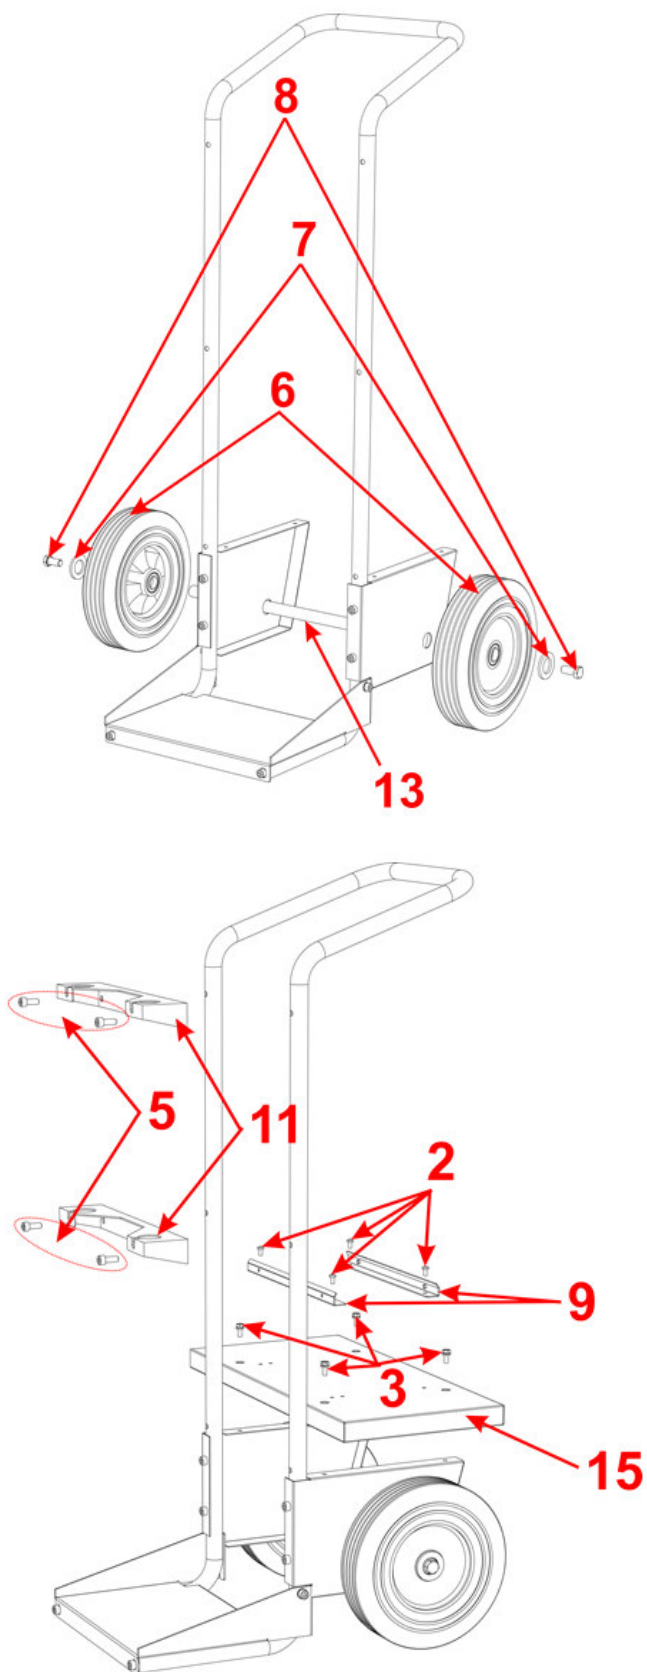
Montage des Schweißgerätswagens Schritt 2 & 3
